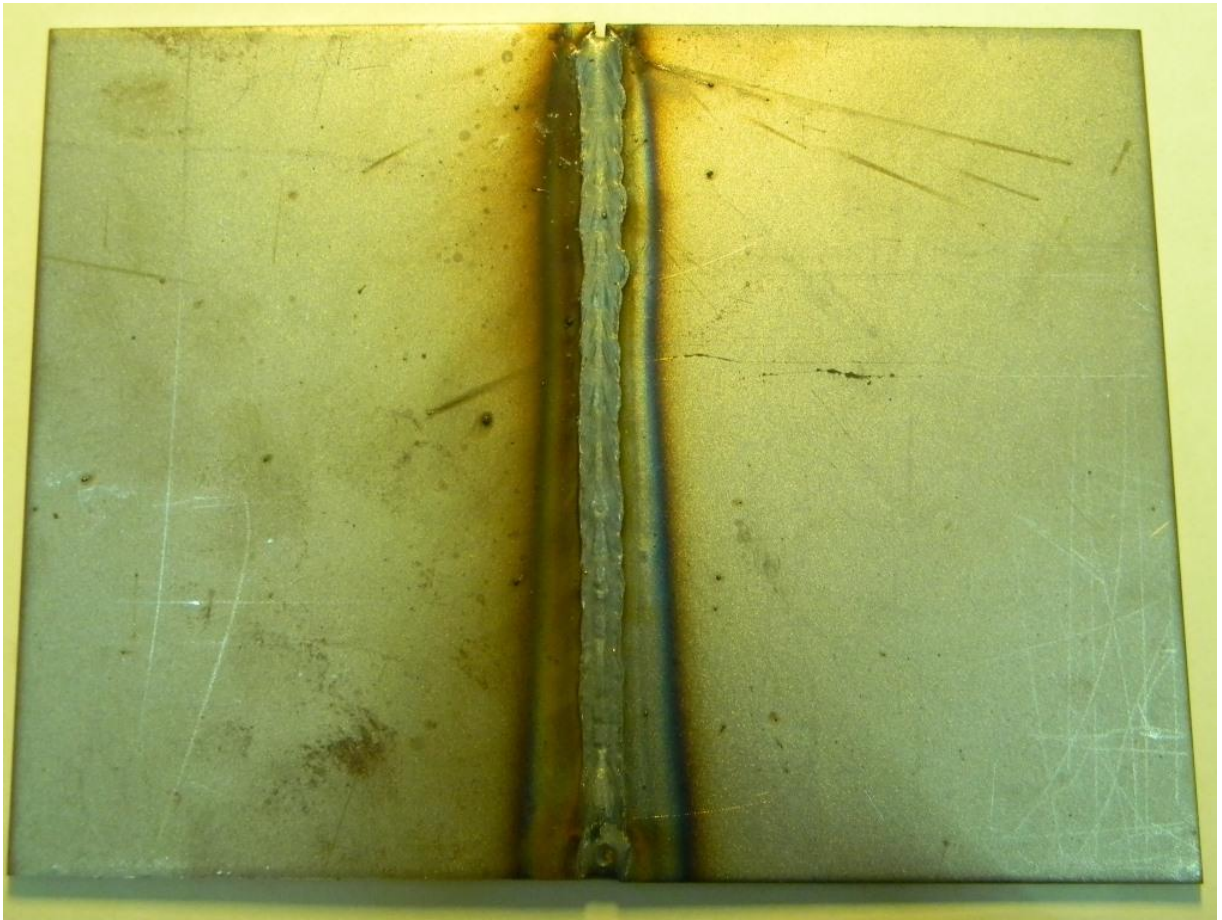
Образец после сварки подготовленный вырубкой с EPS
